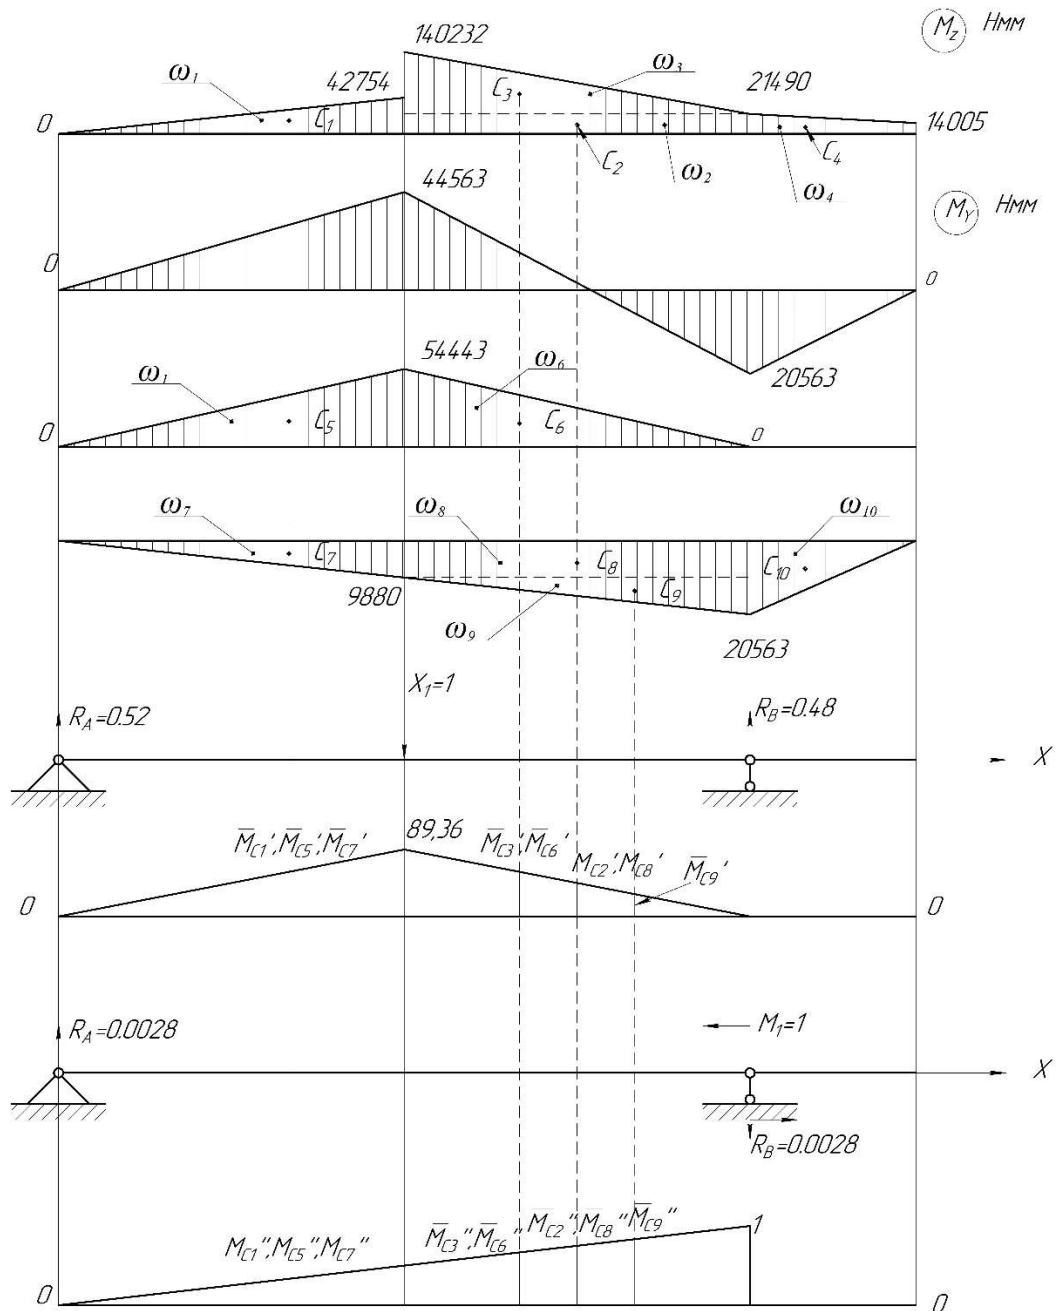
Розрахункові схеми швидкохідного вала редуктора
